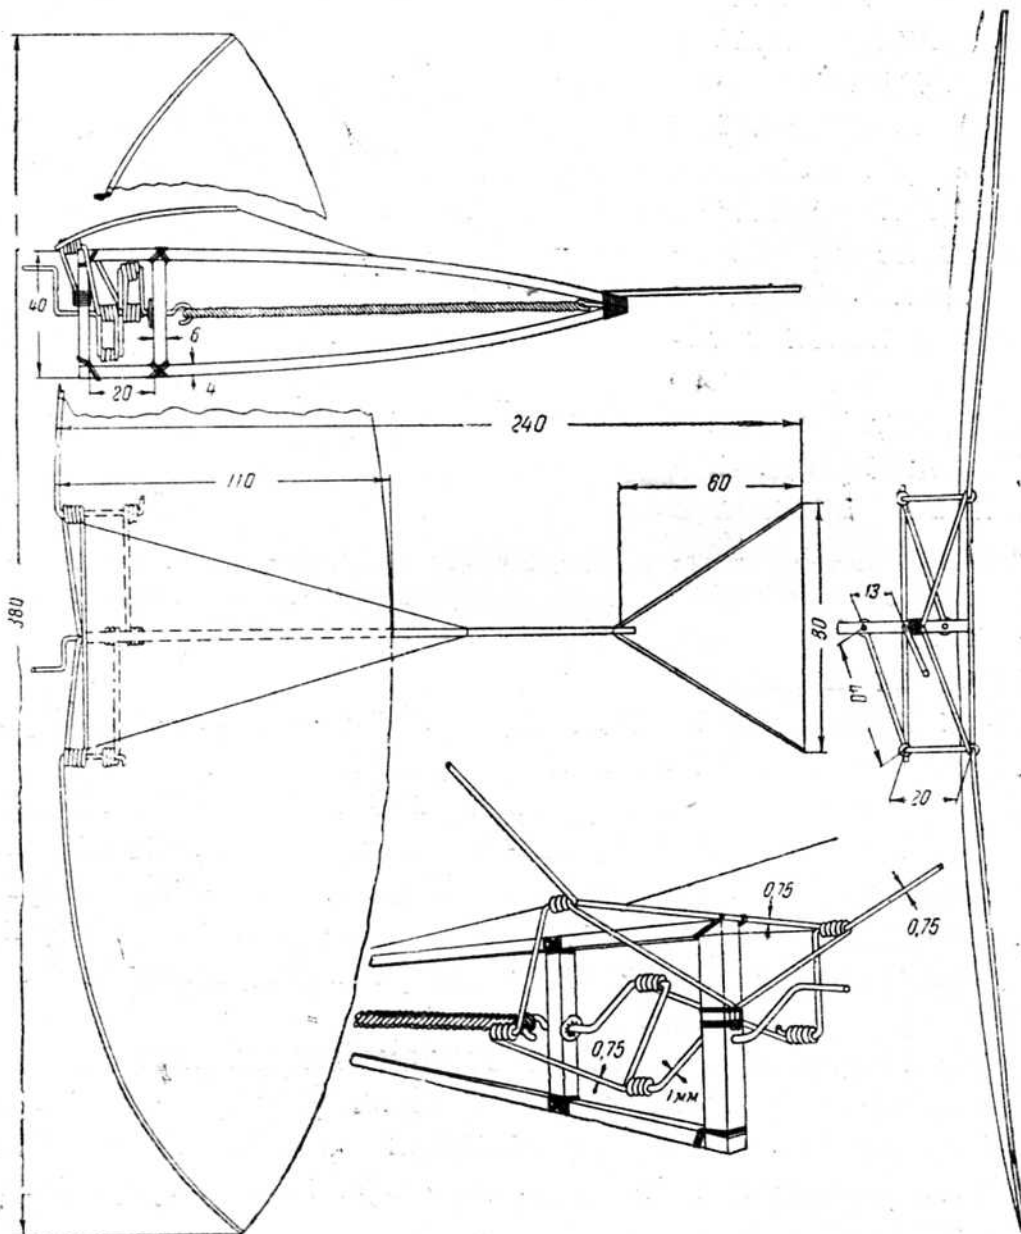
Общий вид проволочной модели с шелковой обтяжкой
